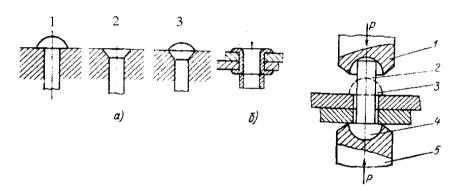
Виды заклепочных соединений: а – стержневые; б – трубчатое; 1 – с полукруглой головкой; 2 – с потайной головкой; 3 – с полупотайной головкой
